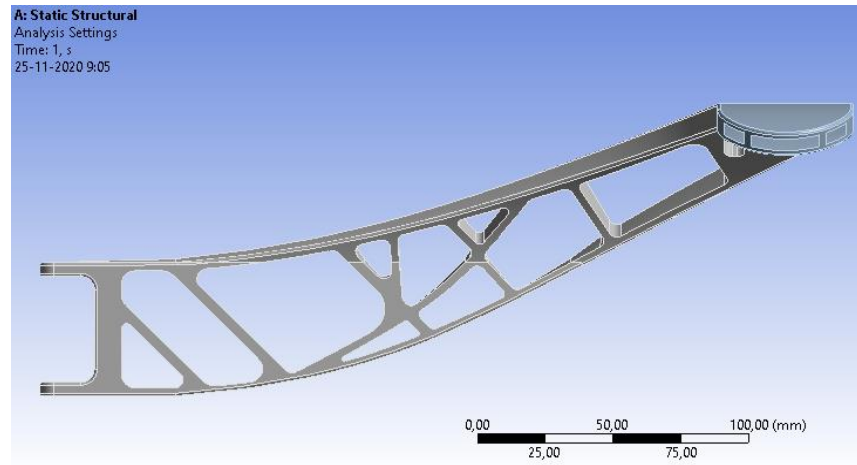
Vista 3 rediseño N°2 de eslabón pierna izquierda.
